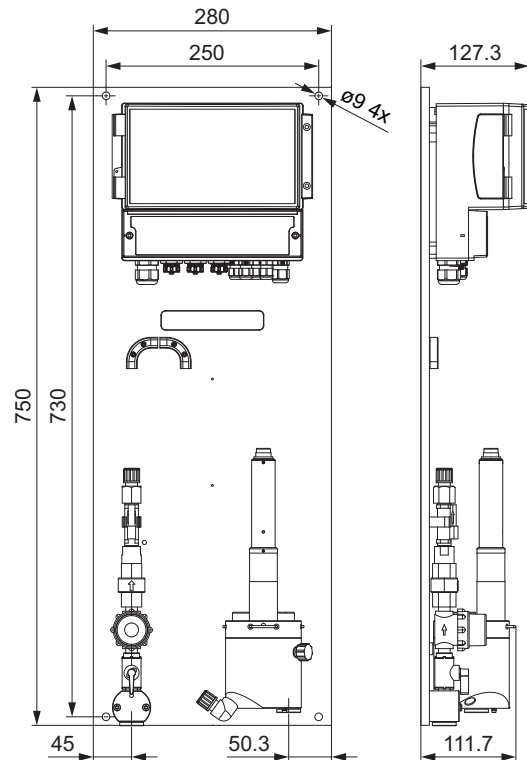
Abmessungen (in mm) des DID mit Durchflusszelle, Installationsausführung BF3 für bis zu drei Sensoren
